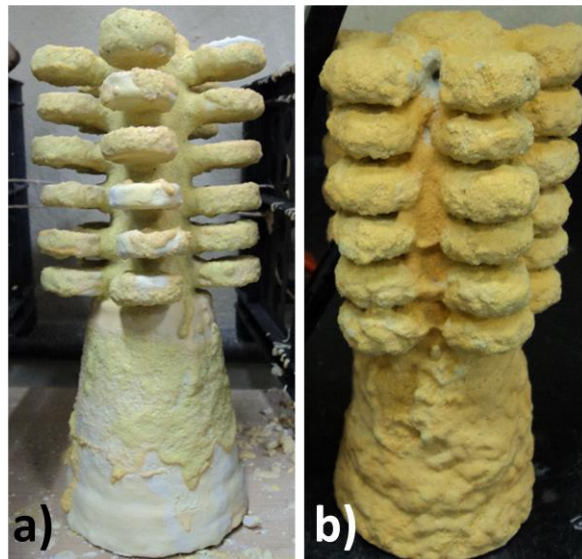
a) Primera capa del investimento # 1 al molde #1, b) Molde # 1 listo para descerar. Nótese el orificio en la parte superior del molde.
